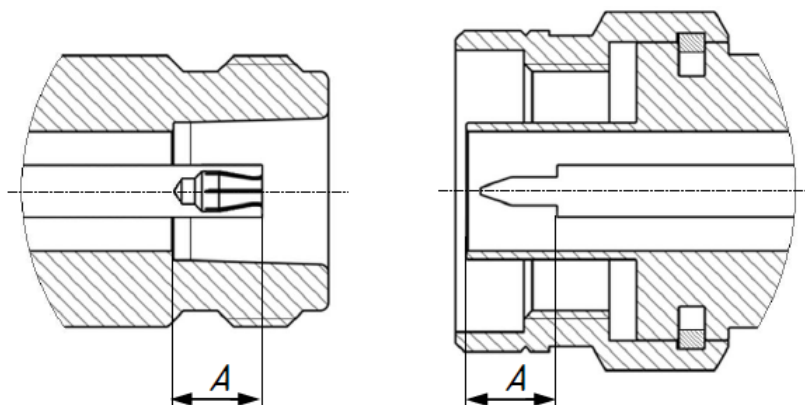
Соединители тип N и III (розетка и вилка)
